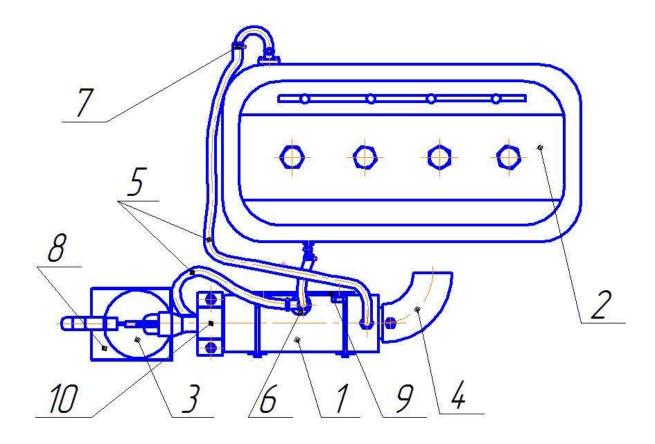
Разрабатываемая конструкция предпускового подогревателя
